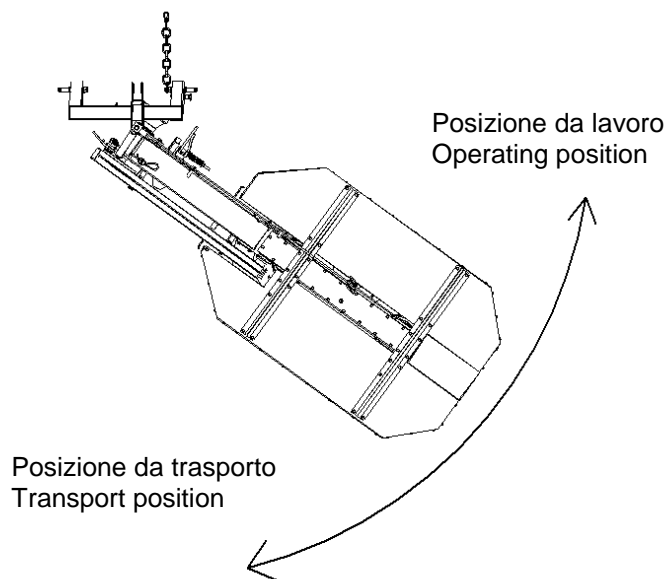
barra falciante in posizione da lavoro - posizione da trasporto
